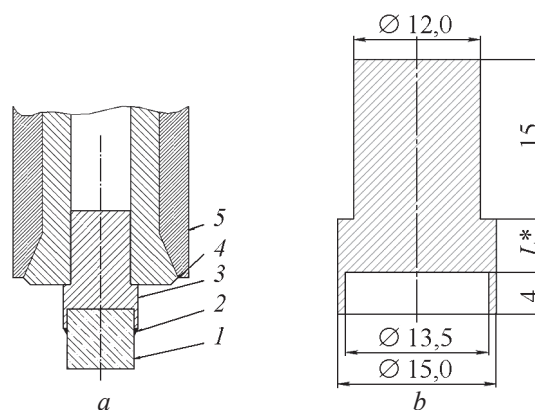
a* — схема крепления твердосплавного резца в цанге: 1 — твердосплавный элемент, 2 — серебряный припой, 3 — державка, 4 — цанга, 5 — оправка цанги; *b* — эскиз оправки.
